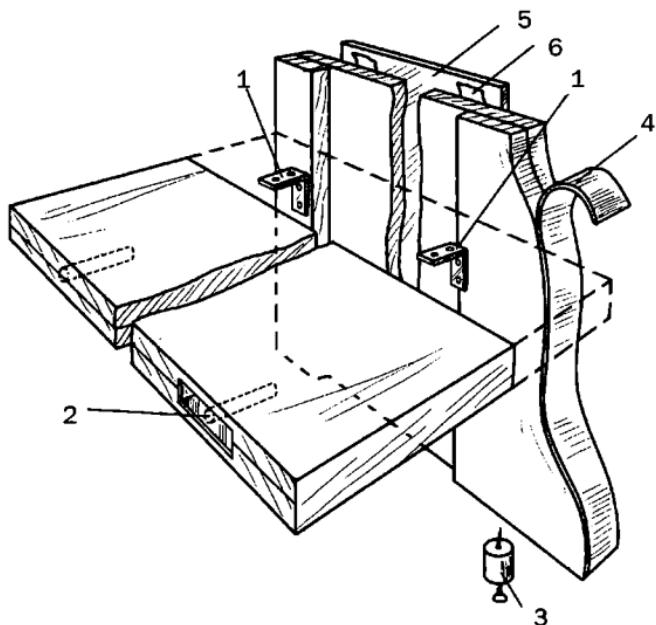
Схема крепления полок: 1 — уголки-стяжки; 2 — отверстия под полкодержатели; 3 — ножка; 4 — кромочная обкладка; 5 — зеркало; 6 — двухсторонний скотч
